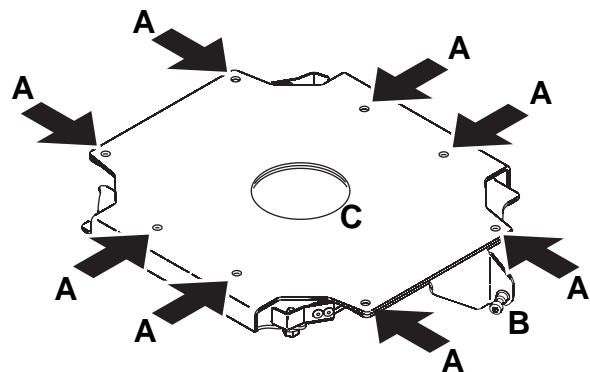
Montagepunkte des Schnellbefestigungs-Adapters
